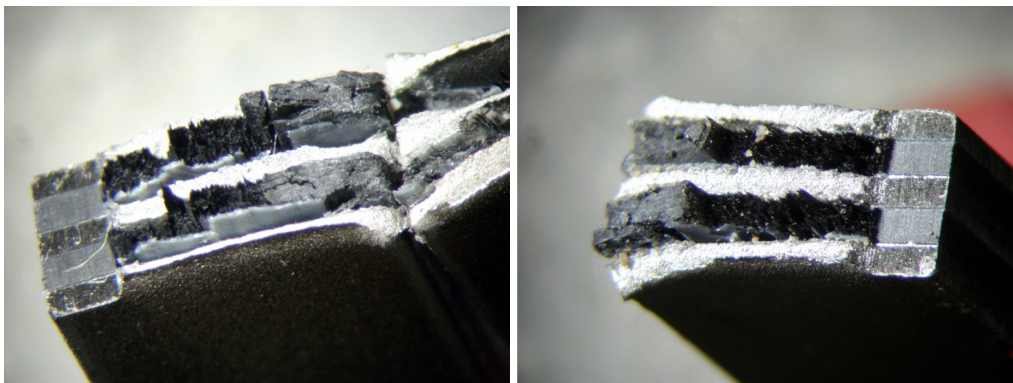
Detalhe das superfícies de fratura e da composição do laminado.
